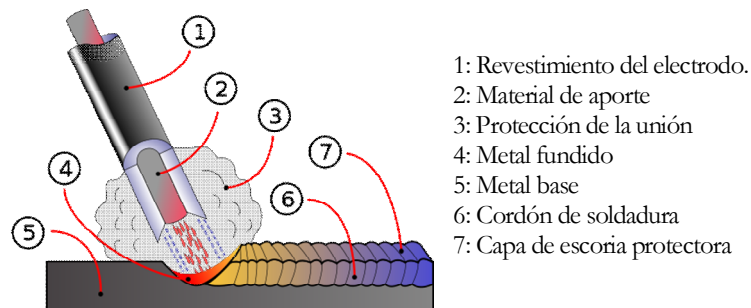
Esquema del proceso de formación del cordón de soldadura [58].
